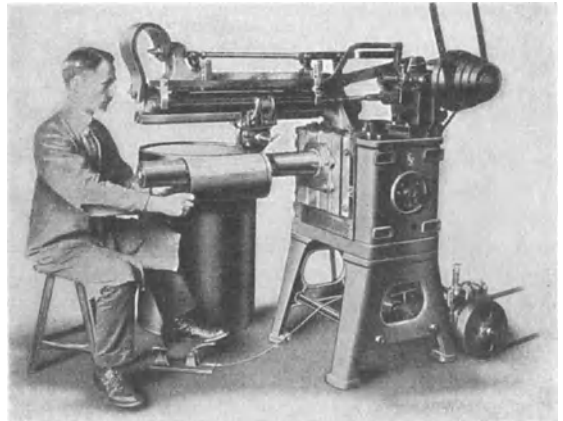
Rollenschritt-Nahtschweißmaschine mit Wanderrolle.
